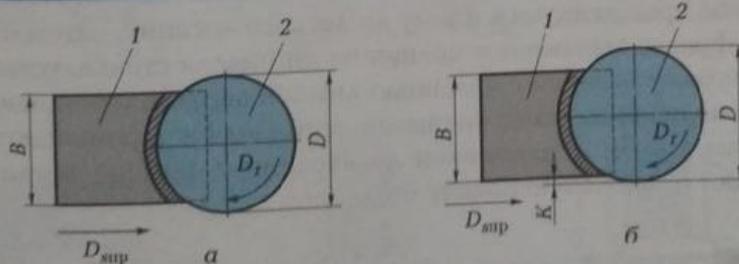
Схемы фрезерования торцевой фрезой:
